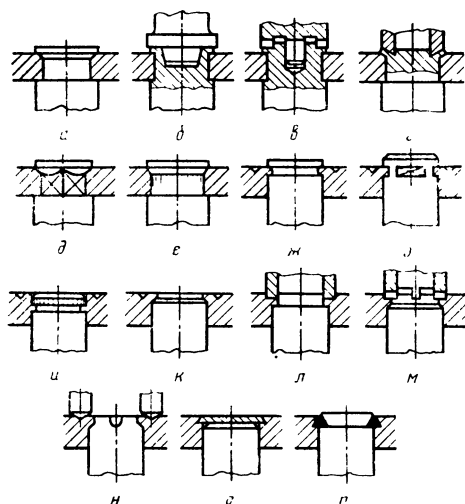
Крепление осей и пальцев в пластинчатых деталях
